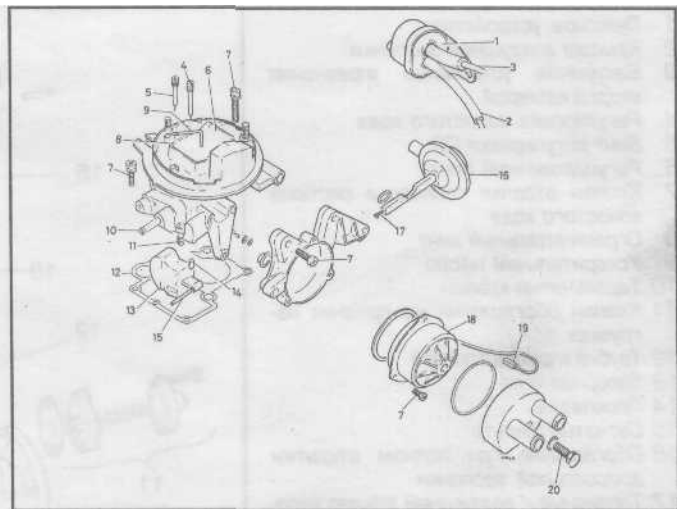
, в. Детали корпуса карбюратора Pierburg / Solex 1B3
